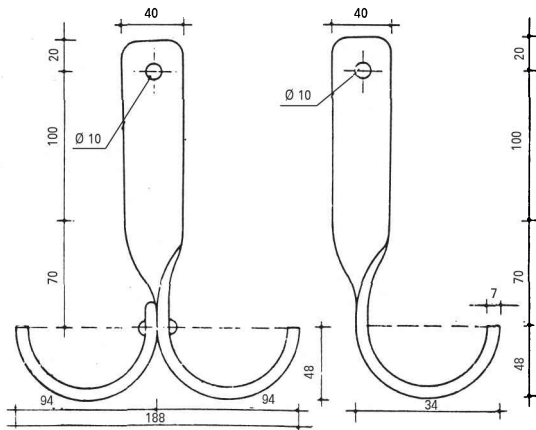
Galerías de Servicio. Detalle de palomillas tipos II y III.
